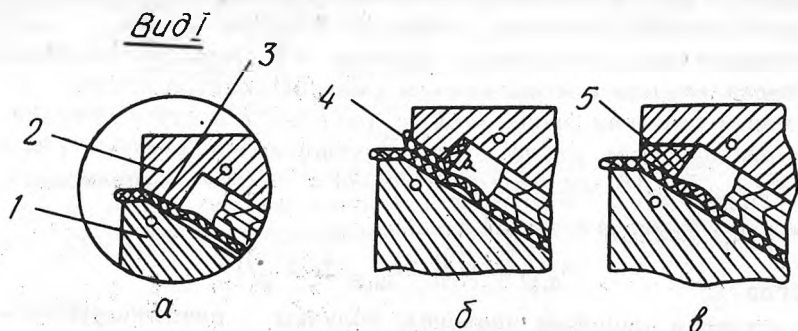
Конструкция бортов вакуумных пресс-форм: а—жесткий из металла; 2—комбинированный из резины и металла; в—эластичный из резины; 1—матрица; 2—пуансон; 3—эластичная диафрагма; 4—эластичная часть борта; 5—эластичный борт.
